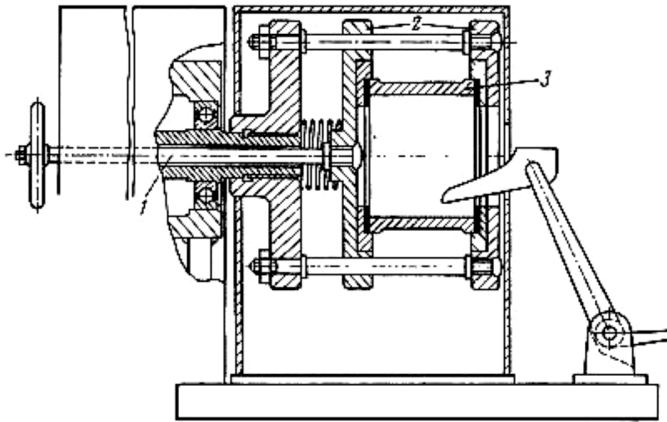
Верстат для відцентрової заливки підшипників:
